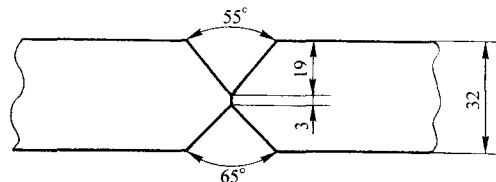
分离器焊接坡口形式与尺寸
